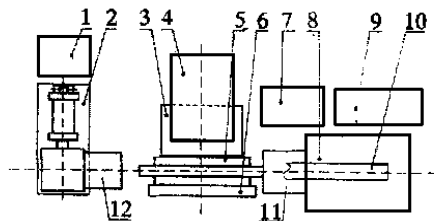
LC2024-03F 载重斜交轮胎成型机平面布置图
